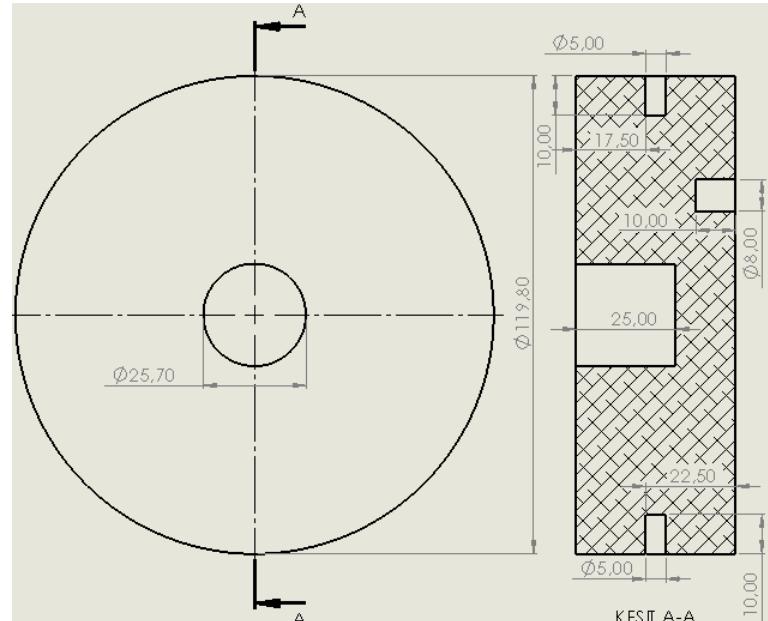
Motor Durdurucu Halkası Montaj 1
